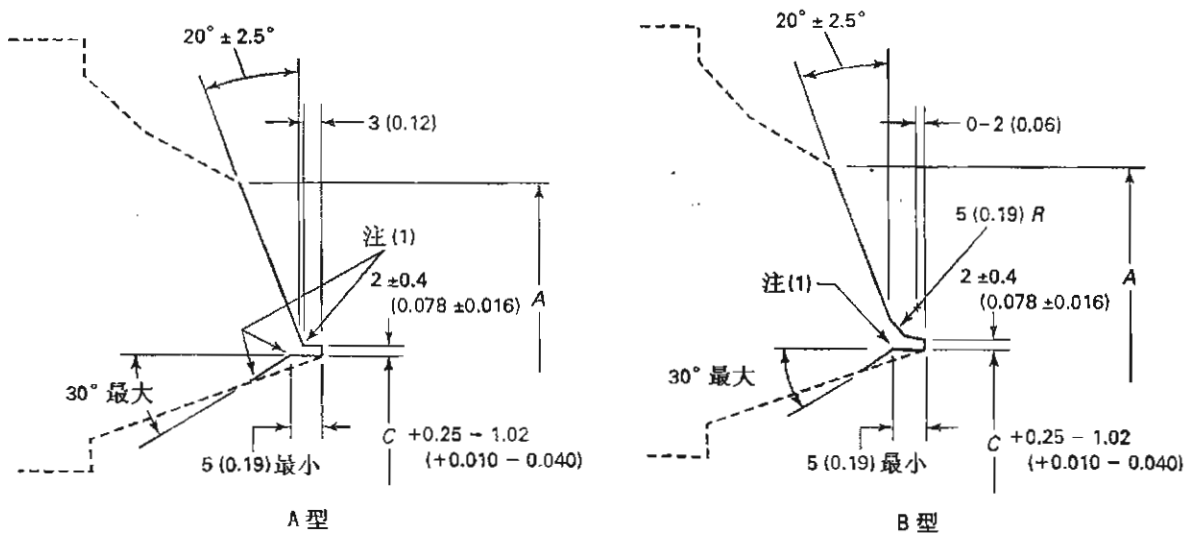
壁厚 > 22mm (0.88 英寸) 的焊接坡口细部图
